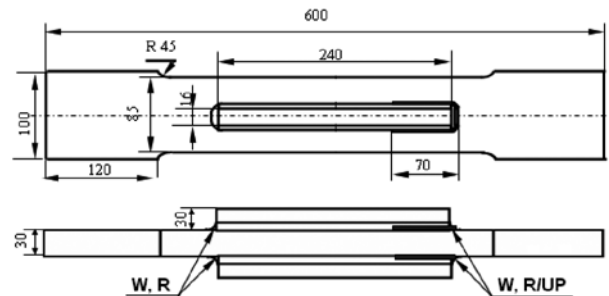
種々の状態で疲労試験を行った溶接継ぎ手試験片形状 (W—As weld, R—ガウジング後の補修溶接, R/UP—ガウジングと補修溶接後の UP 処理)
